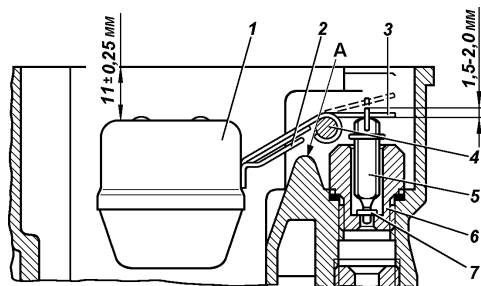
Поплавок карбюратора К-151Л и его регулировка:
